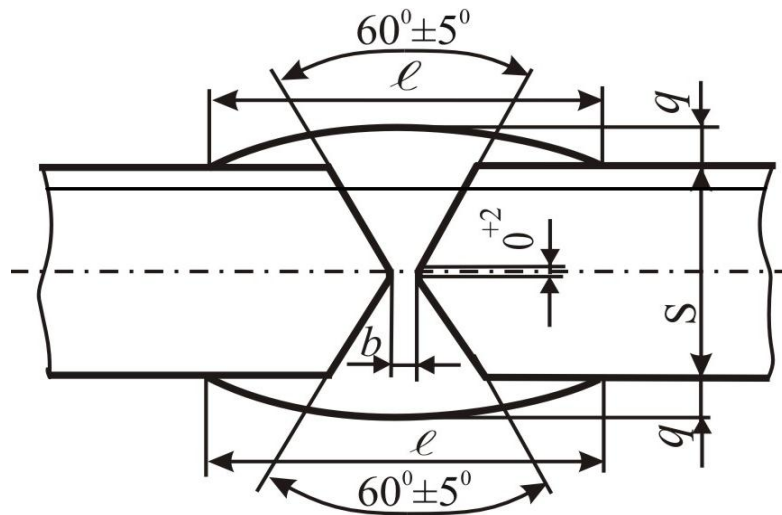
Конструктивные элементы сварного соединения
